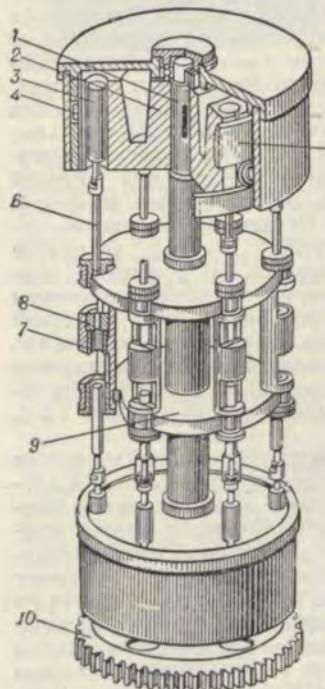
Схема двухстороннего механического ротора: 1 — вал ротора; 2 — барабан; 3 — ползун; 4 — ролик ползуна; 5 — неподвижная кривая; 6 — пuhanсон; 7 — корпус блока инструмента; 8 — матрица; 9 — блокодержатель; 10 — приводная шестерня.
